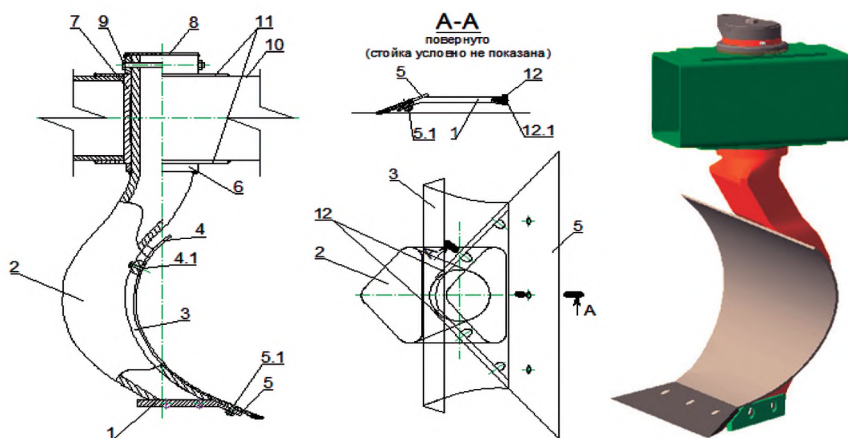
Симметричный ромбовидный корпус рабочего органа поворотного плуга
